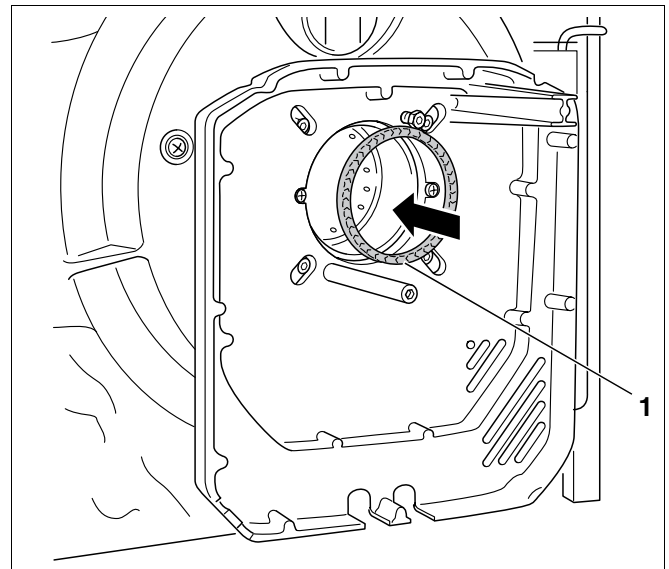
Mise en place du joint sur les modèles de brûleur 17 à 45
